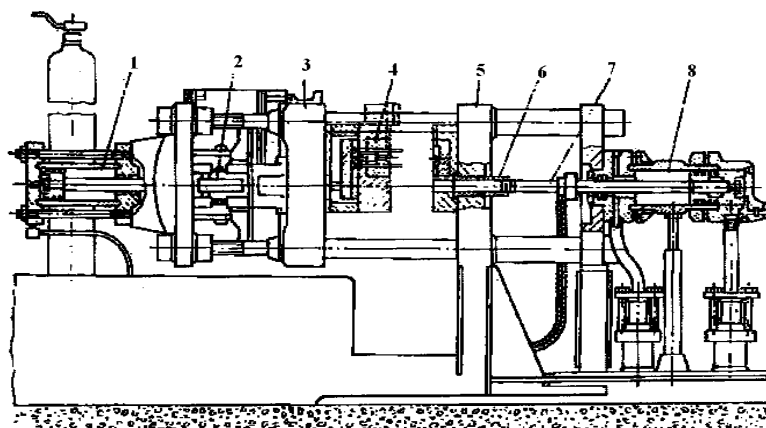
Поршнева машина з холодною горизонтальною камерою пресування: 1,8-гідроциліндр; 2-запірний механізм; 3-рухома плита машини; 4-рухома напівформа; 5-нерухома плита машини; 6-заливочний стакан; 7-пресуючий поршень.
